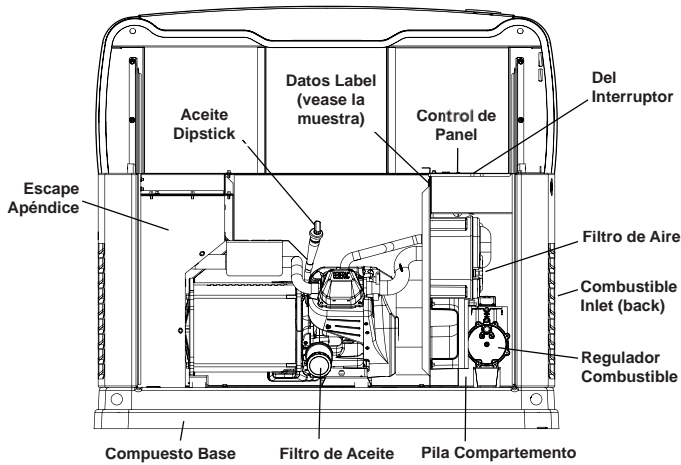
Motor GT-530 de 10kW, de dos cilindros en V (con la puerta desmontada)
